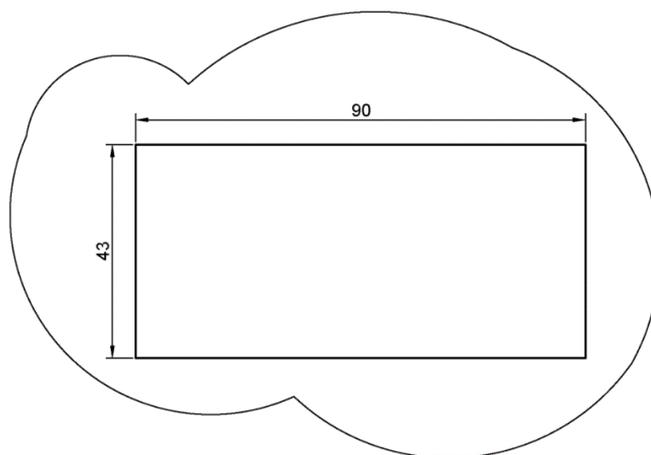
Габаритные размеры монтажного отверстия для установки модуля
